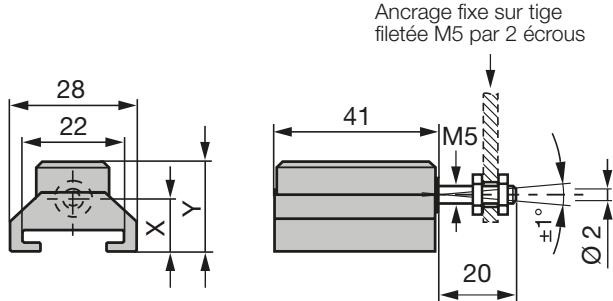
Dimensions de montage du capteur de position BTL5-M/N-2814-1S
